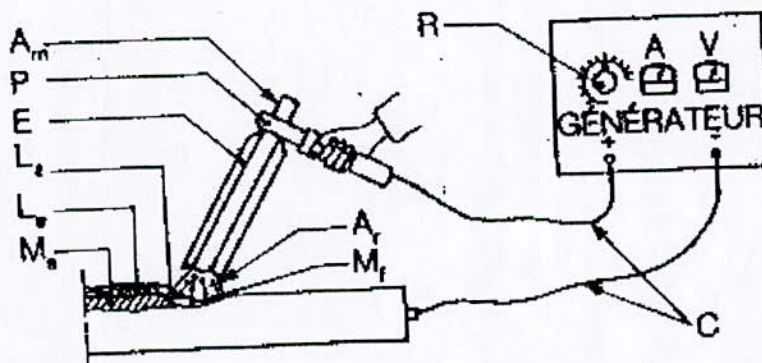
Procédé de soudage à l'électrode enrobée
